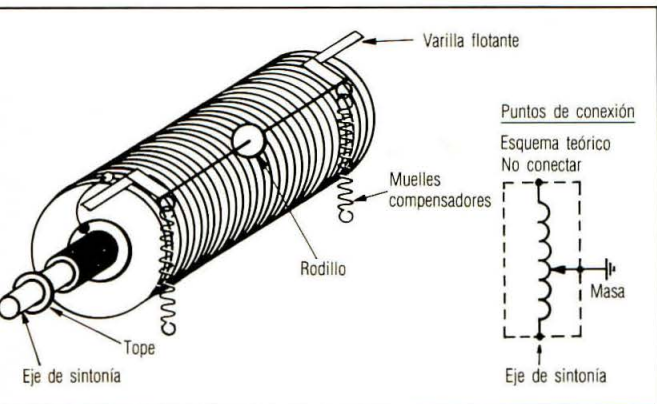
Detalle de la bobina, eje de sintonía y rodillo deslizante montado en la varilla flotante.
